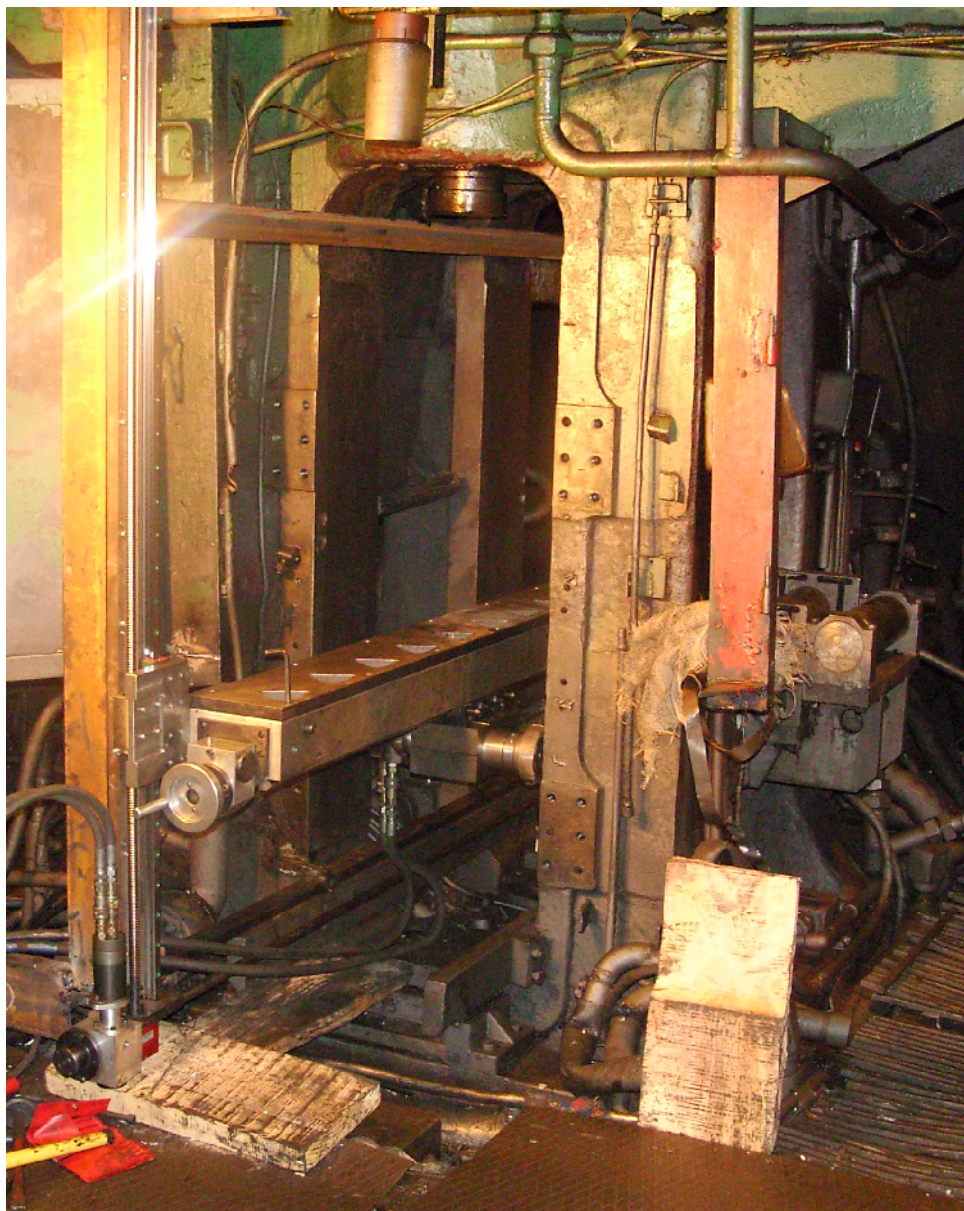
Мобильный фрезерный станок, установленный в проем станины клетки прокатного стана
